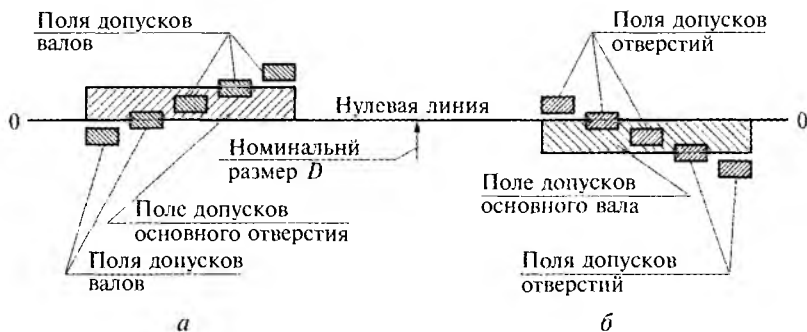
Примеры расположения полей допусков для посадок в системе отверстия (а) и вала (б)
